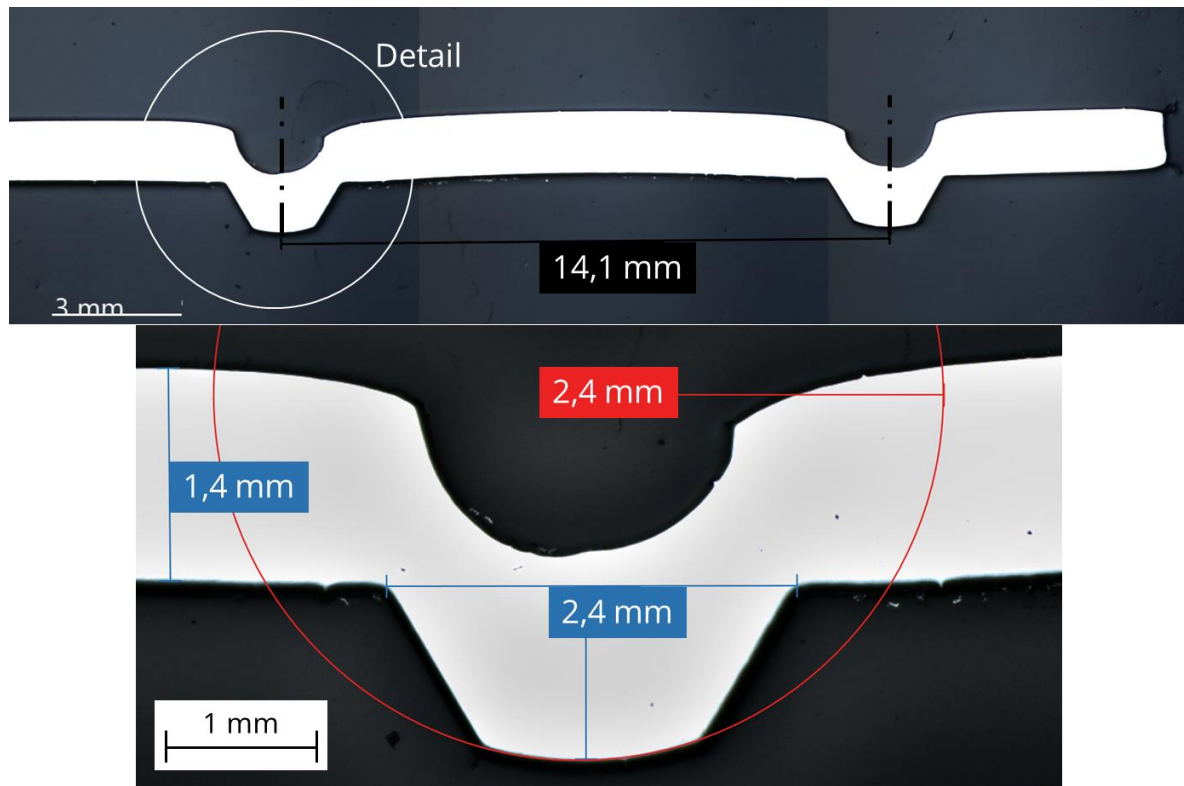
Querschliff geprägter Buckel – spitzer Buckelwinkel
